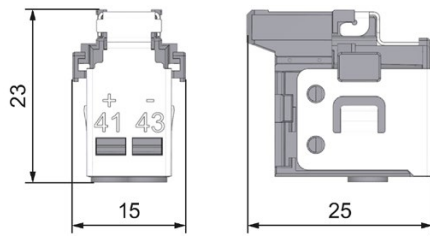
Maßbild Einspeiseelement für 25 mm-Module
